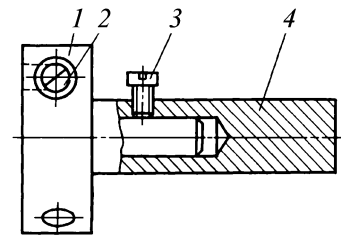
Быстропереналаживаемое приспособление для крепления резцов:
